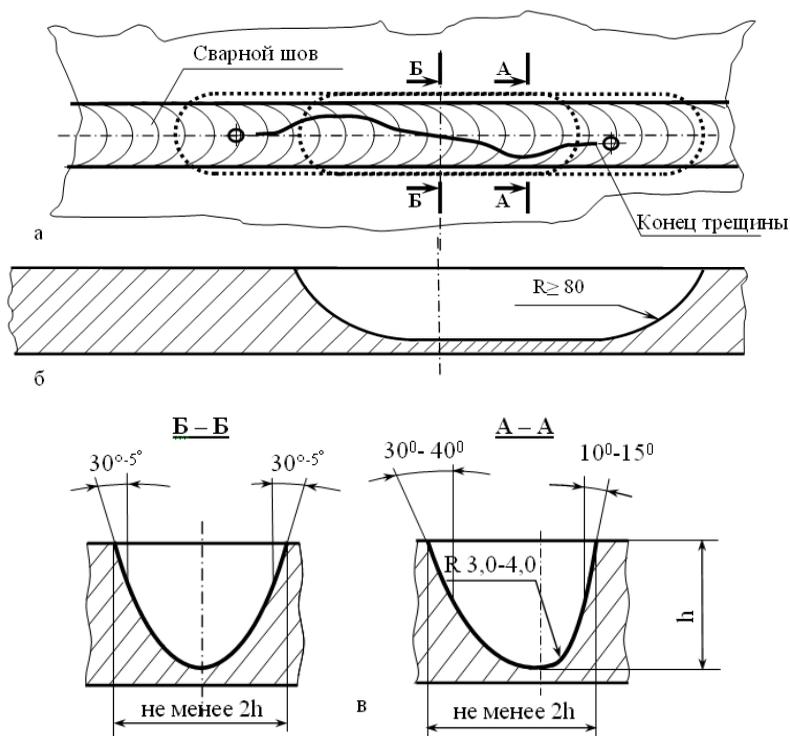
Подготовка шва с трещиной к ремонту: а – трещина в шве; б – профиль выборки вдоль трещины; в – профиль выборки в поперечном сечении
